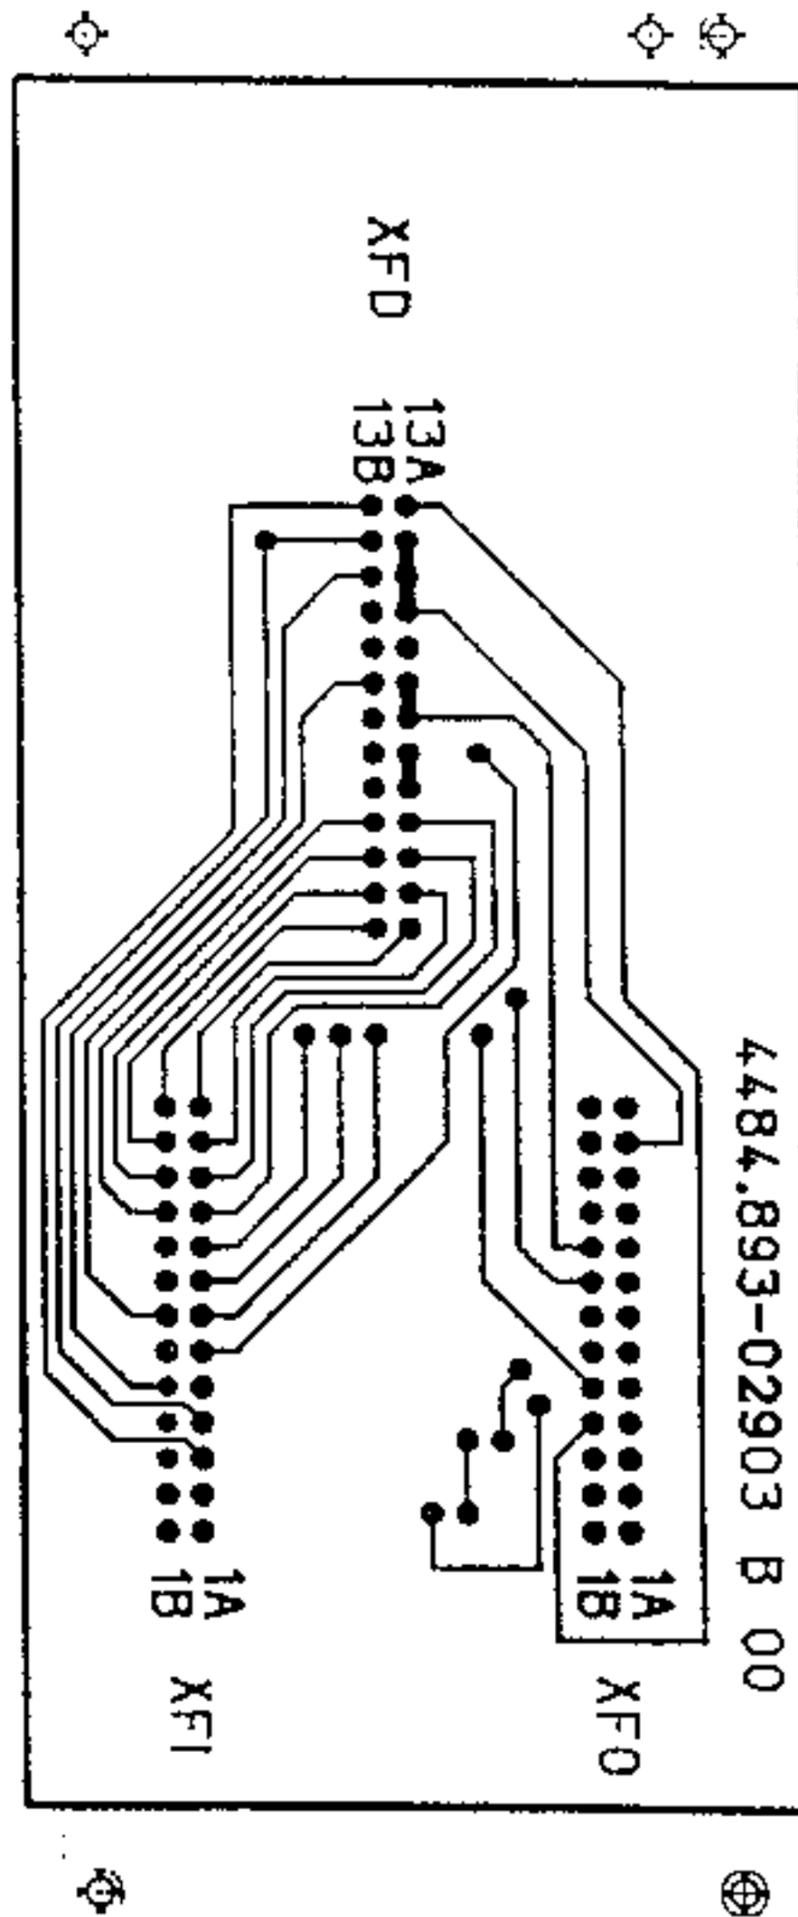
Leiterplatte gemäß Zeichnungs-Nr. 4484.893-02903
